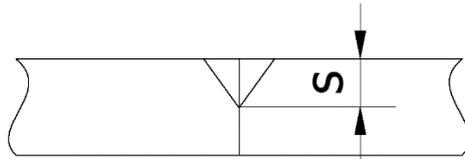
Profundidad del cordón en soldadura a tope
